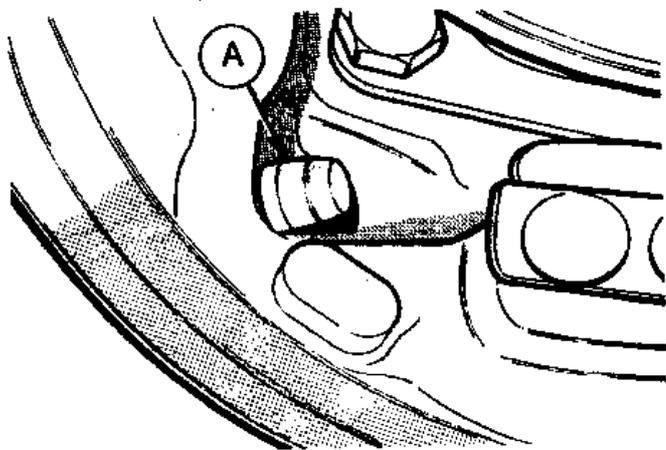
Упор рычага ручного тормоза (A) (Разд.9)
